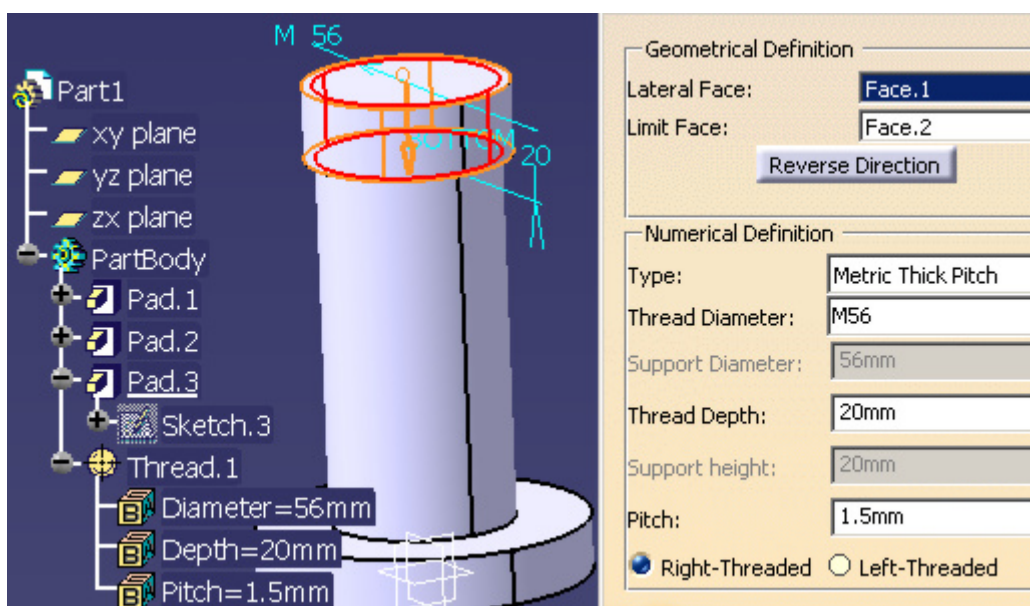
Executarea filetului de prindere pe capătul corpului robinetului
